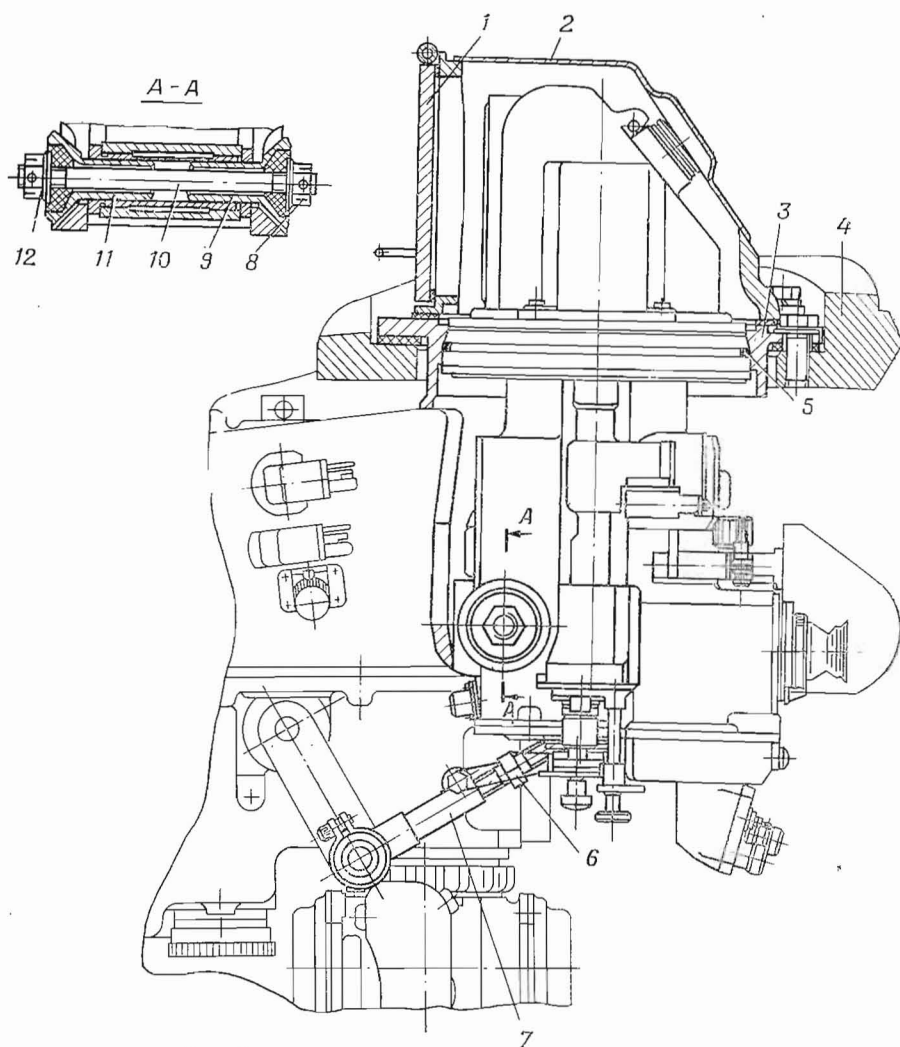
Установка ночного прицела ТПНЗ-49:
